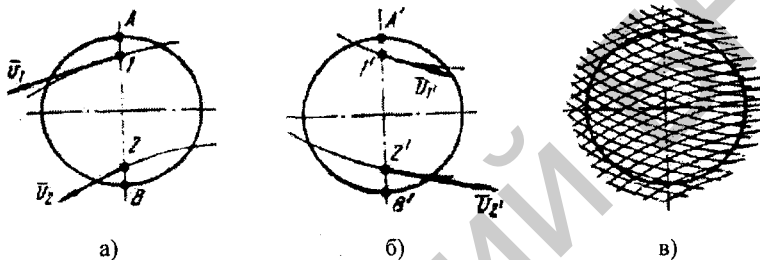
Схема нанесения следов режущего инструмента на обрабатываемую поверхность: а, б – формирование обрабатываемой поверхности на входе рабочей зоны и выходе из нее; в – сетка следов инструмента на сферической торцовой поверхности после обработки
